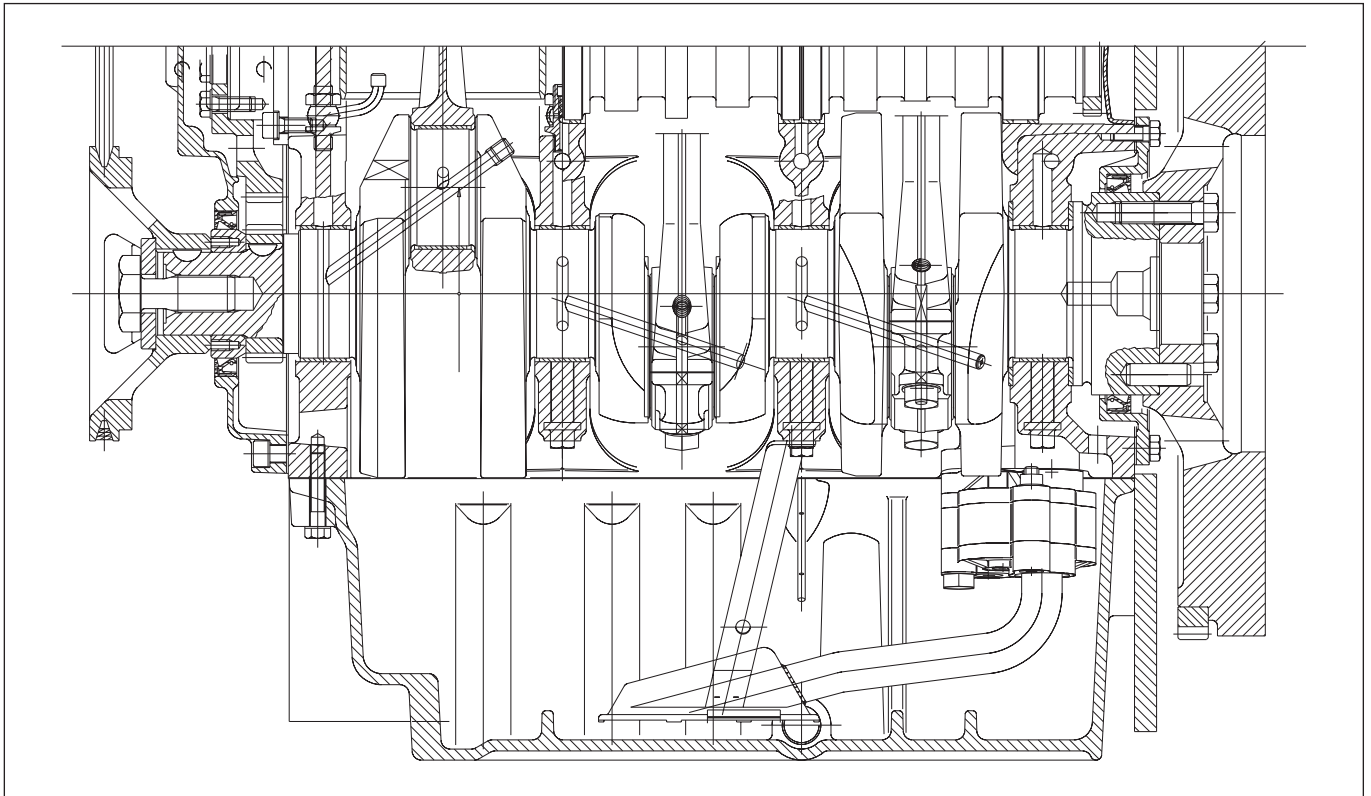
Vue d'ensemble du vilebrequin avec moteur 3 cylindres.
